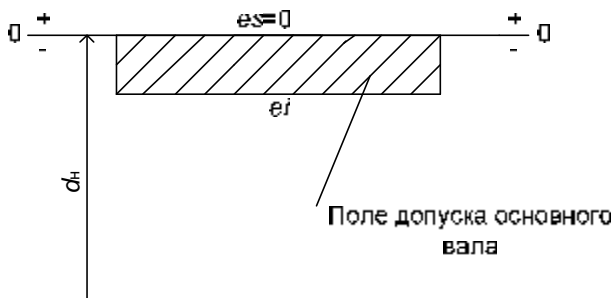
Пример изображения поля допуска основного вала
